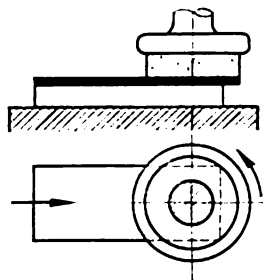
Rectification d'un plan par la face d'une meule boisseau sur une machine à table animée d'un mouvement alternatif
